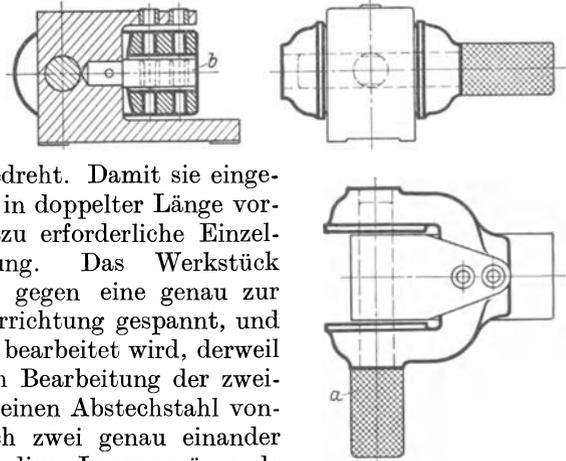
Standbohrspannvorrichtung mit doppelter Werkzeugführung. *a* Entfernung- und richtungbestimmender Bolzen. *b* Aufnahmehorn mit Führungsbüchsen.
